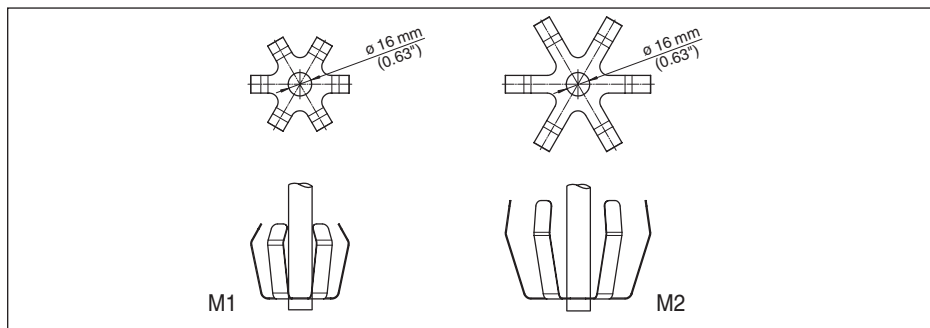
Центрирующие звездочки из металла для стержневых исполнений с \varnothing 16 мм (0.63 in)
